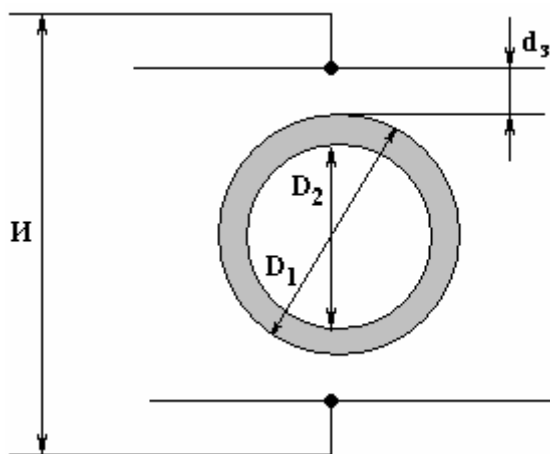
Схема нагрева цилиндрической стеклопластиковой оболочки в конденсаторе с воздушным зазором
